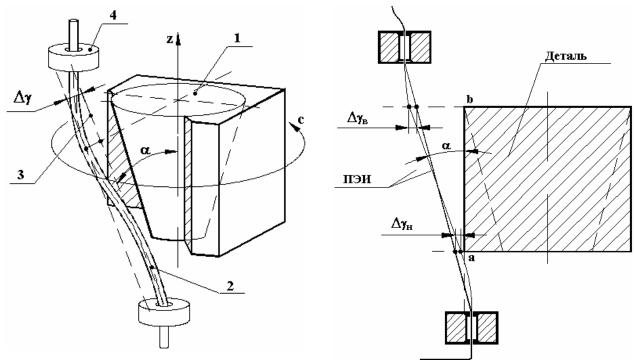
Схема обработки конических поверхностей на четырехкоординатном электроэрозионном станке: 1 — обрабатываемая заготовка; 2 — проволочный электрод-инструмент; 3 — теоретическое положение оси ПЭИ; 4 — система направления ПЭИ; α — заданный угол наклона оси ПЭИ относительно поверхности детали; $\Delta \gamma$ — величина смещения ПЭИ от начального положения в точке касания с деталью; c — направление движения электрода-проволоки вокруг оси z
